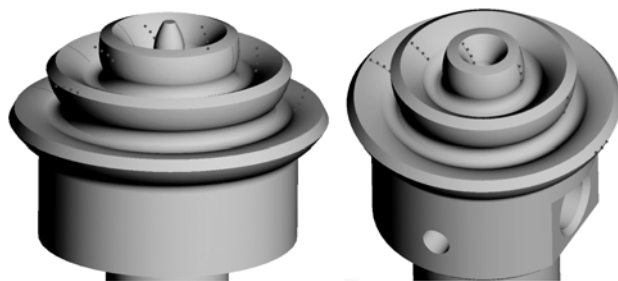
中凸球齿轮和中凹球齿轮接触点轨迹
